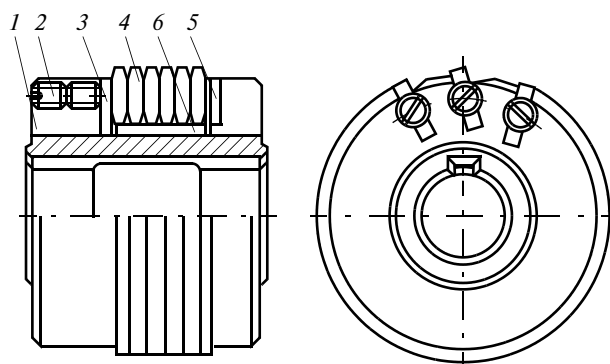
Схема конструкции червячной фрезы с поворотными твердосплавными зубьями-пластинами, позволяющая четырехкратное их использование без переточек: 1 — рабочий корпус фрезы; 2 — винт; 3 — зажимная пластина; 4 — зуб-пластина; 5 — упор; 6 — опорная пластина
